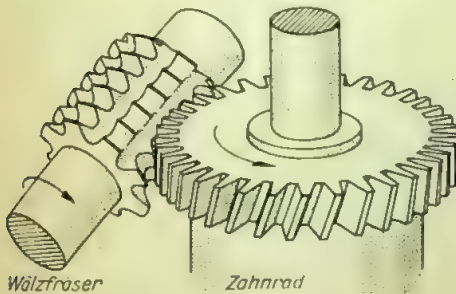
Zahnrad-Wälzfräsen
